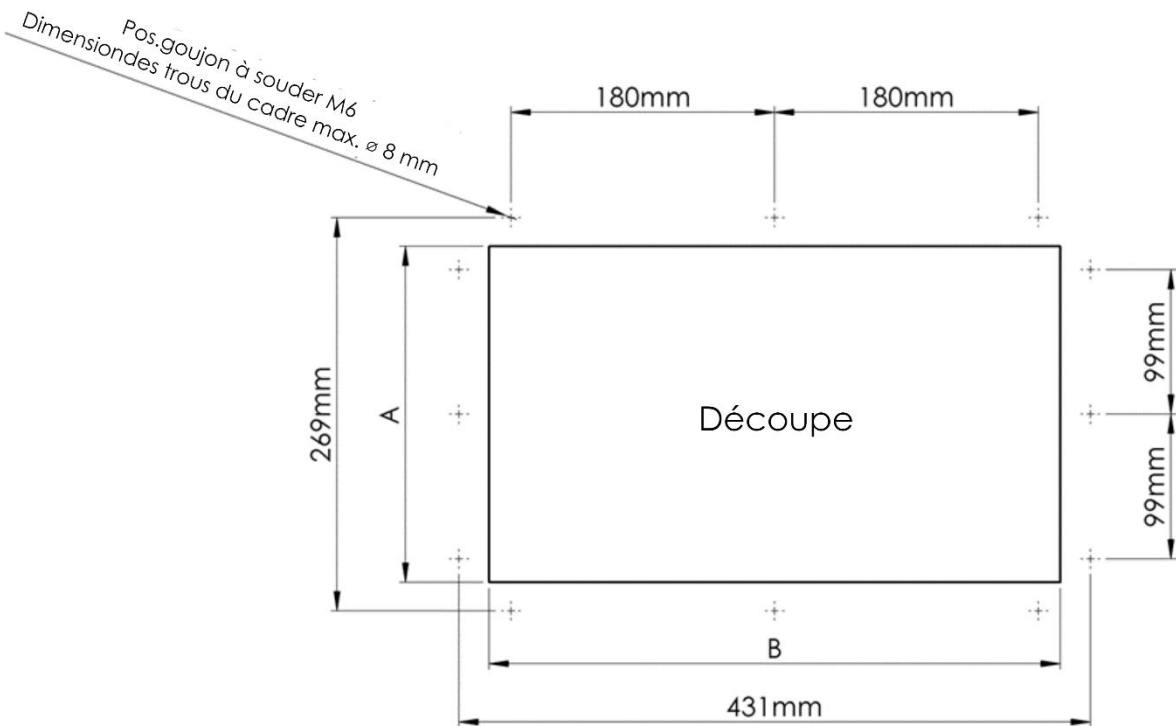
Découpe pour cadre de montage MS-I-20 ES
